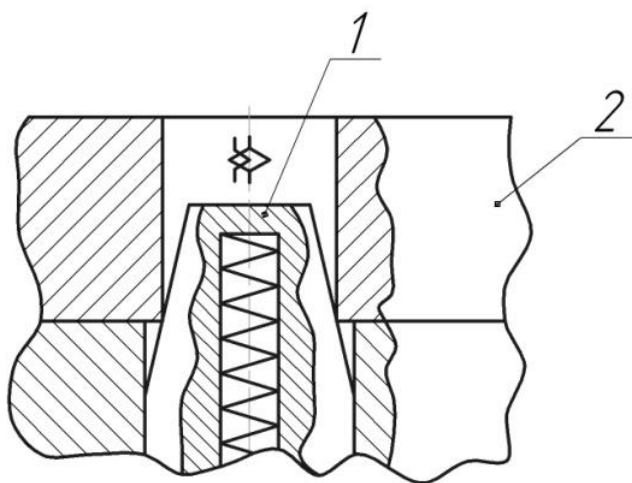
Установка заготовки с помощью конического пальца
